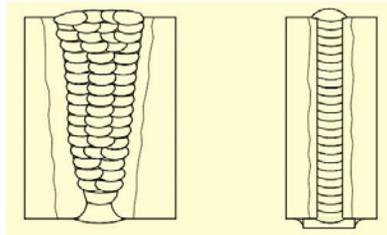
(a) Groove welding, (b) Narrow-gap arc welding
